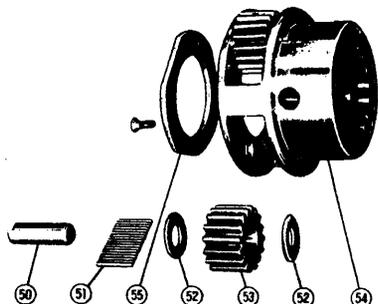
Pièces composant le support des engrenages menés du réducteur épicycloïdal.
